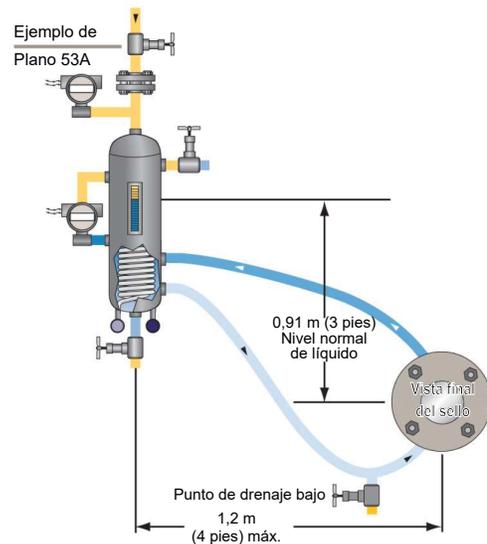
Ejemplo de dimensiones de montaje del Plano 53A de tuberías
